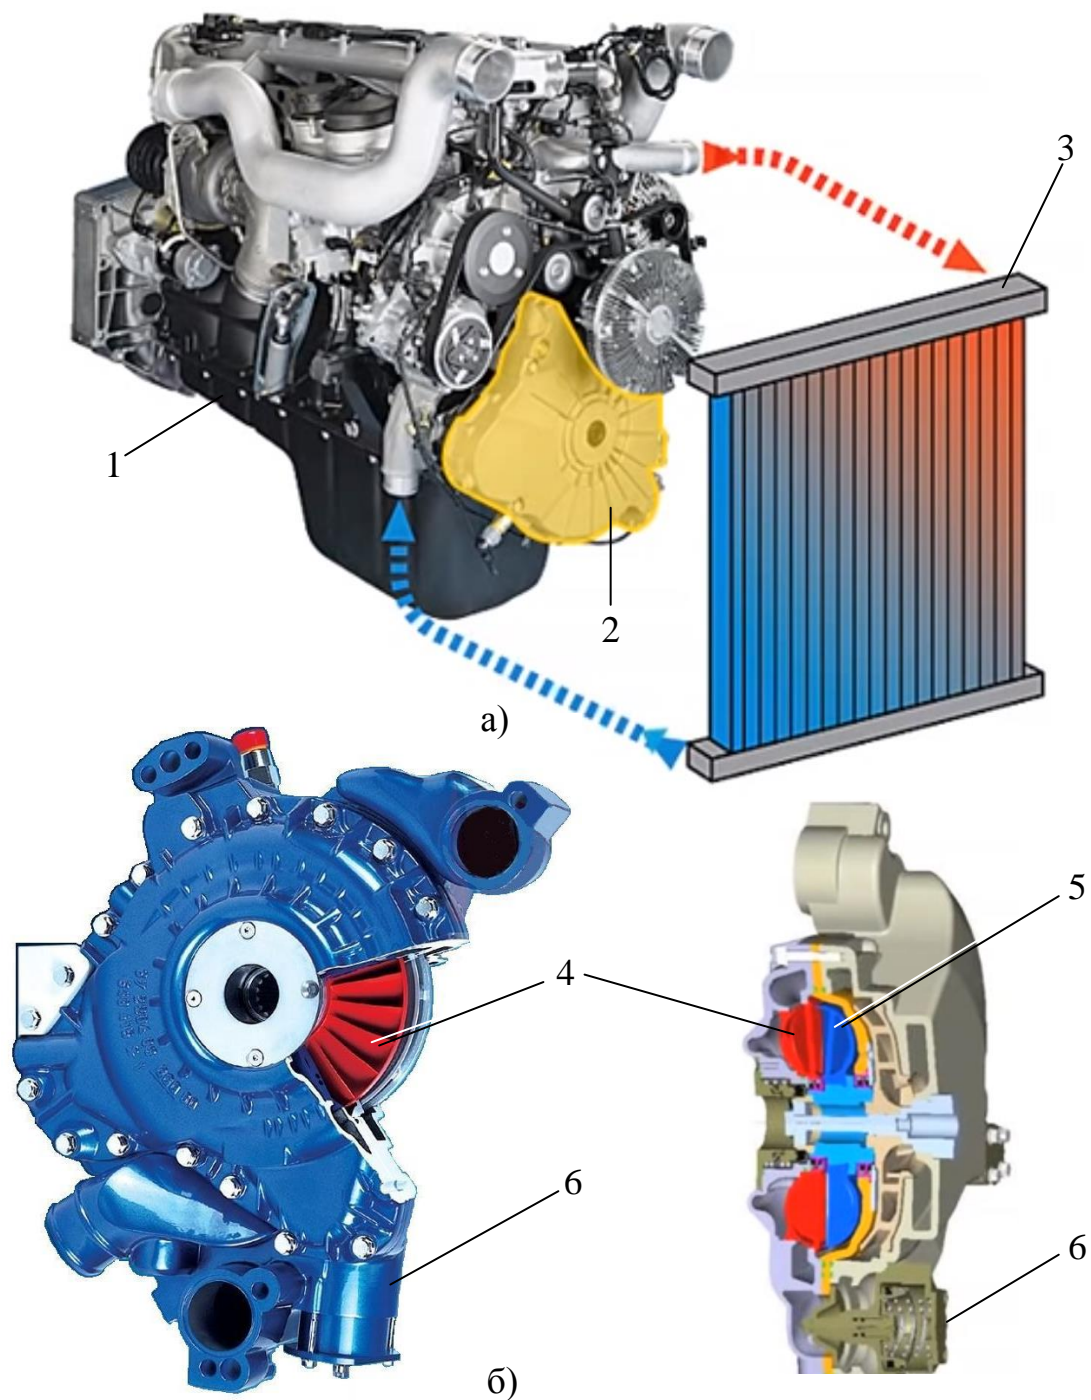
Установка акватардера на двигателе (а), конструкция акватардера (б): 1 – двигатель; 2 – акватардер; 3 – радиатор двигателя; 4 – насосное (подвижное) колесо акватардера, связанное с носком коленчатого вала двигателя; 5 – турбинное (неподвижное) колесо; 6 – управляющий клапан
